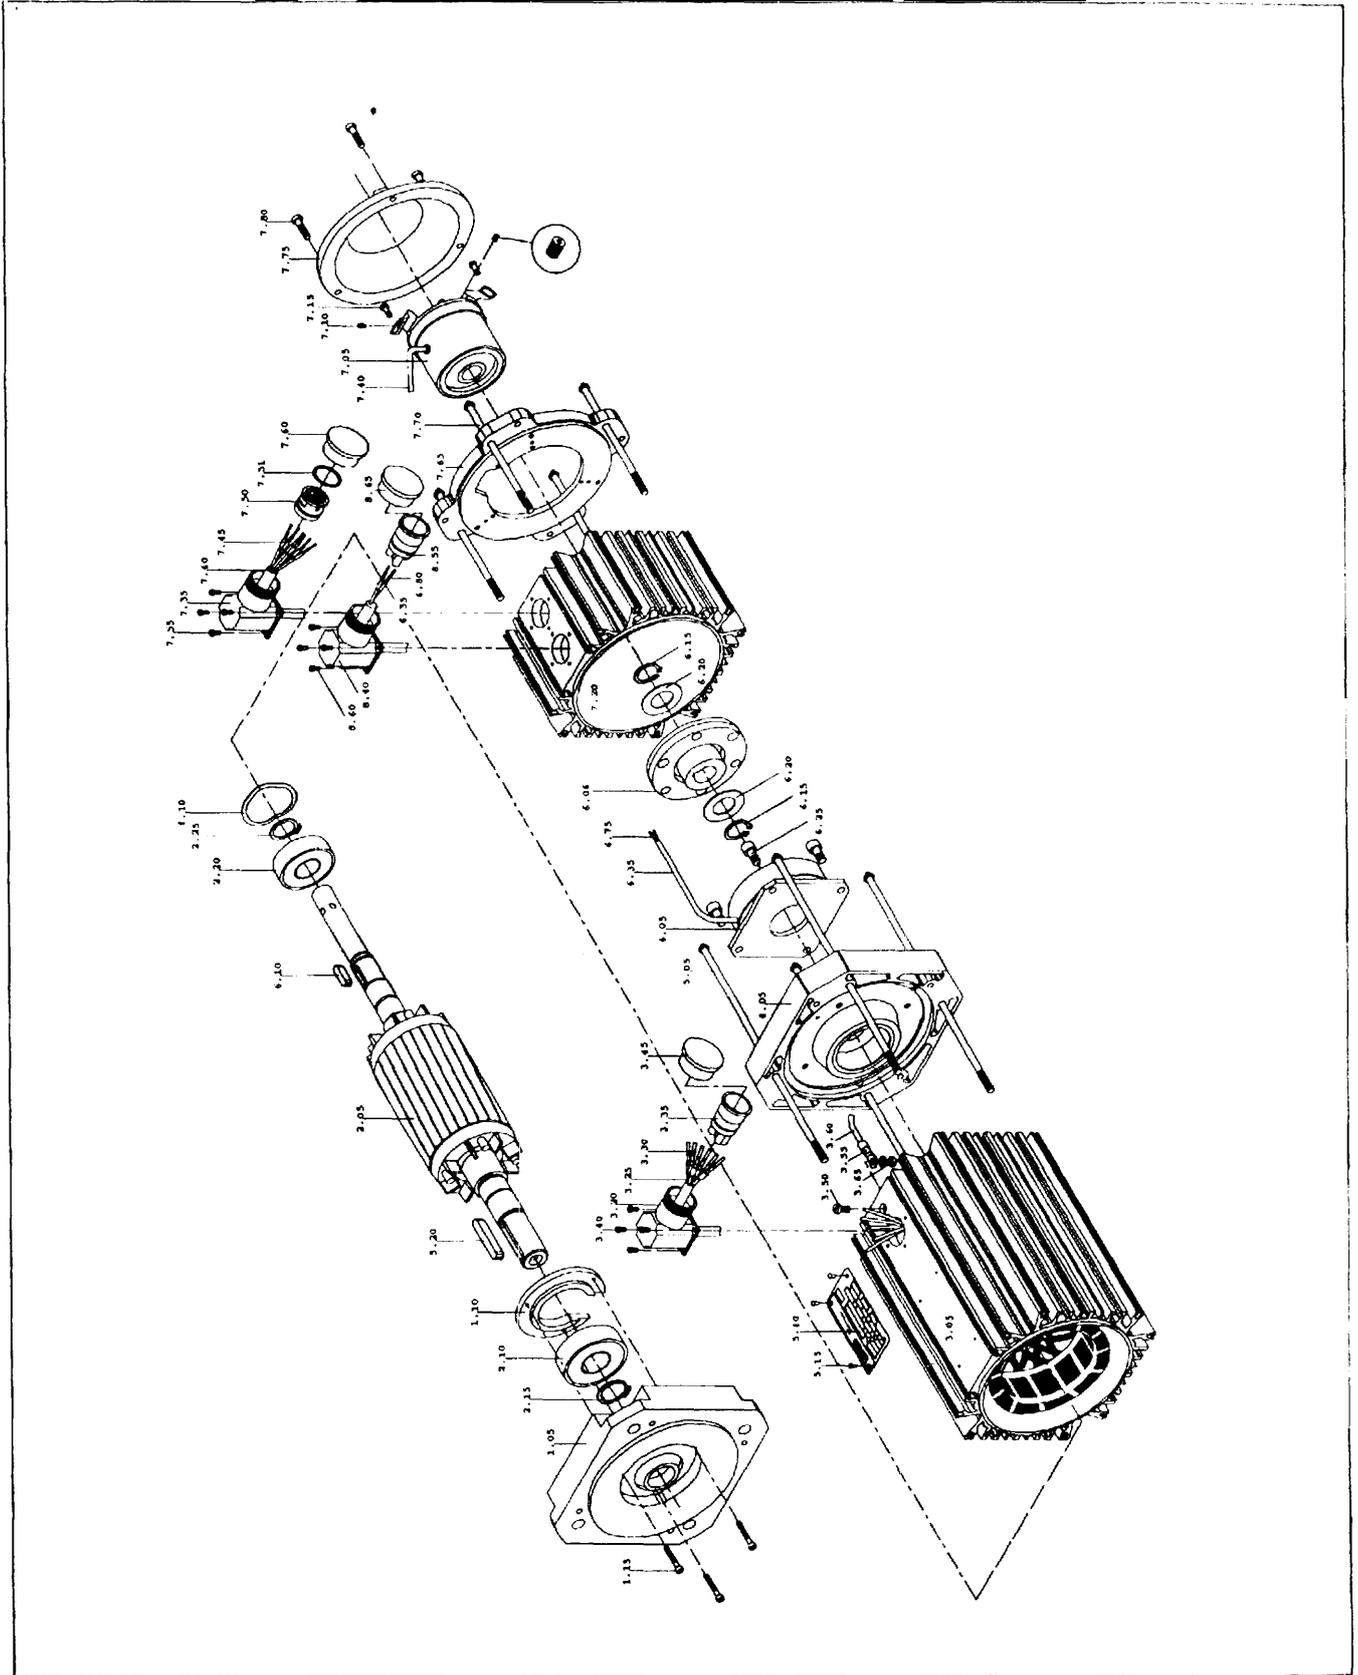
Explosionszeichnung Motor ohne Bremse mit Lüfter DFVARS
